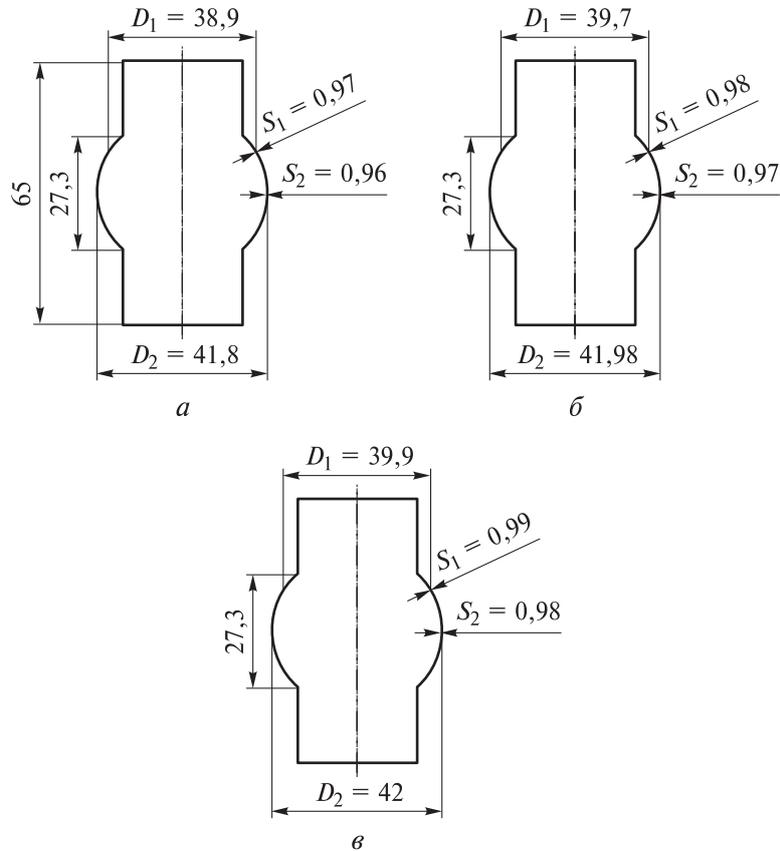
Схема раздачи трубчатой заготовки с использованием внутреннего наполнителя (а) и с подпором (б):
